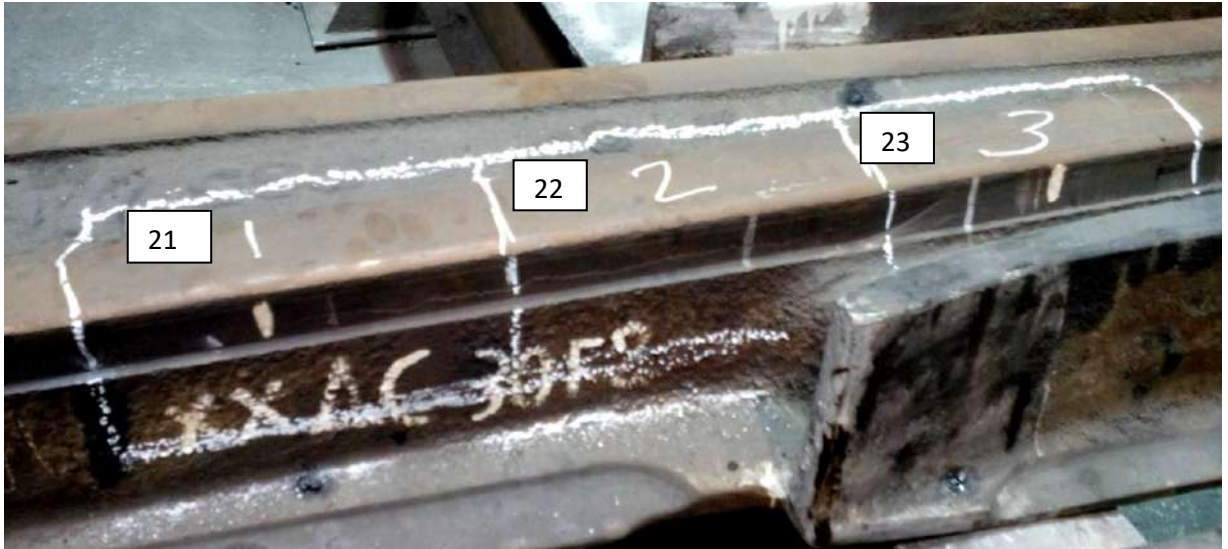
Продольная трещина на боковой поверхности клина литой крестовины с разметкой для отбора образцов
